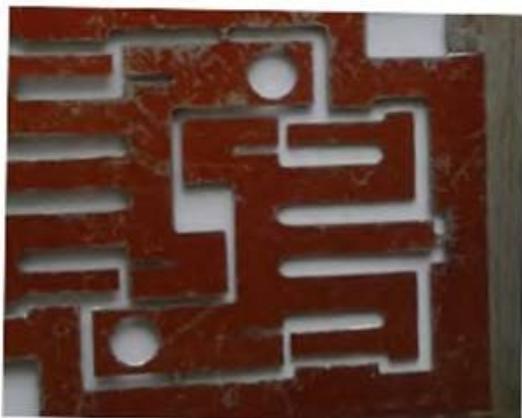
Многослойный шаблон для изготовления деталей из листа
